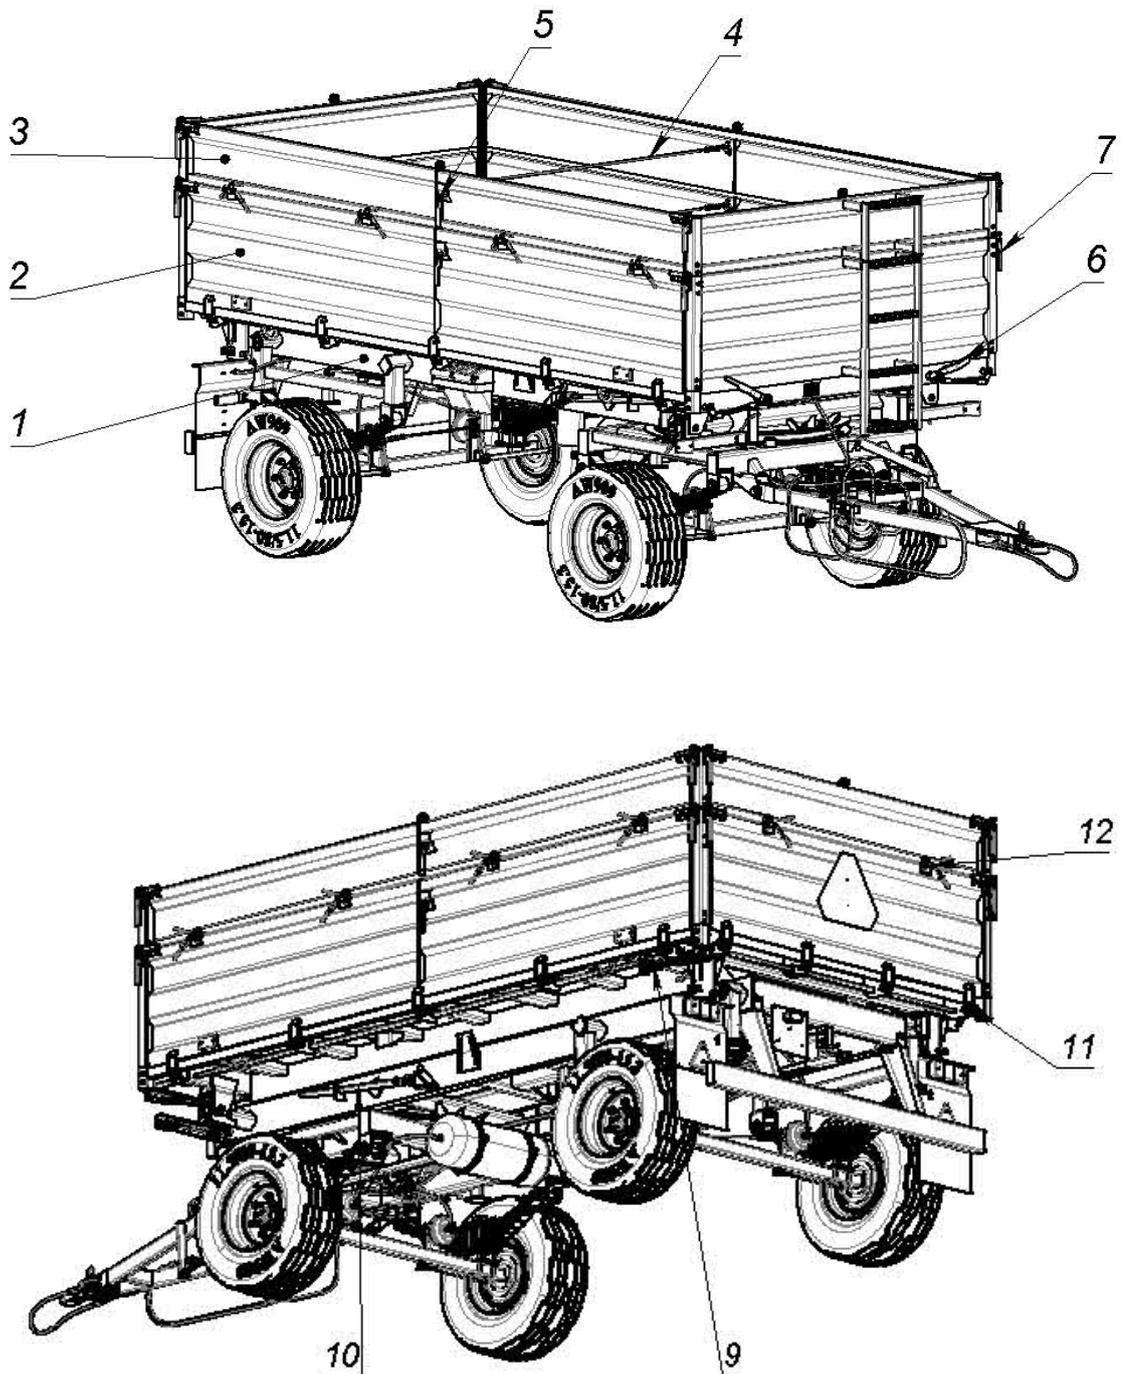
Общий вид прицепа 2ПТС-6,5 «Зерновоз»
